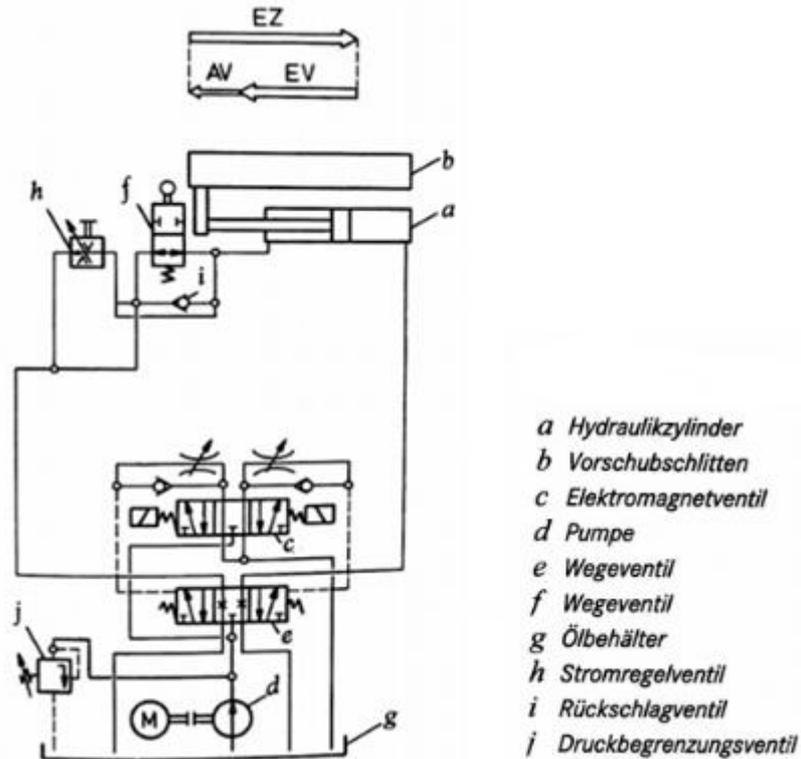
Aufbau einer Hydraulischen Steuerung [Perovic2006, S.533]
